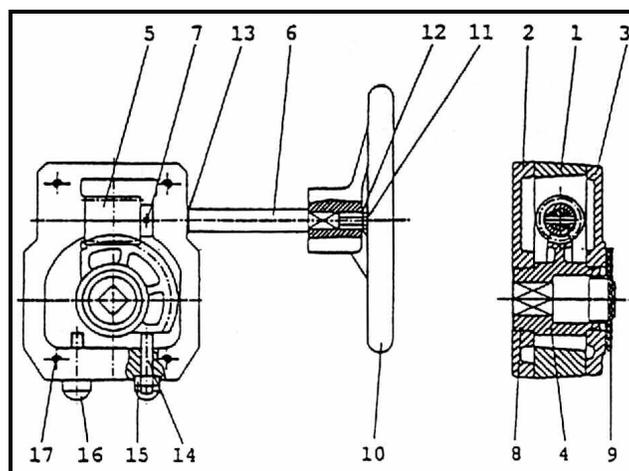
Устройство ручного редукторного привода с червячной передачей.
